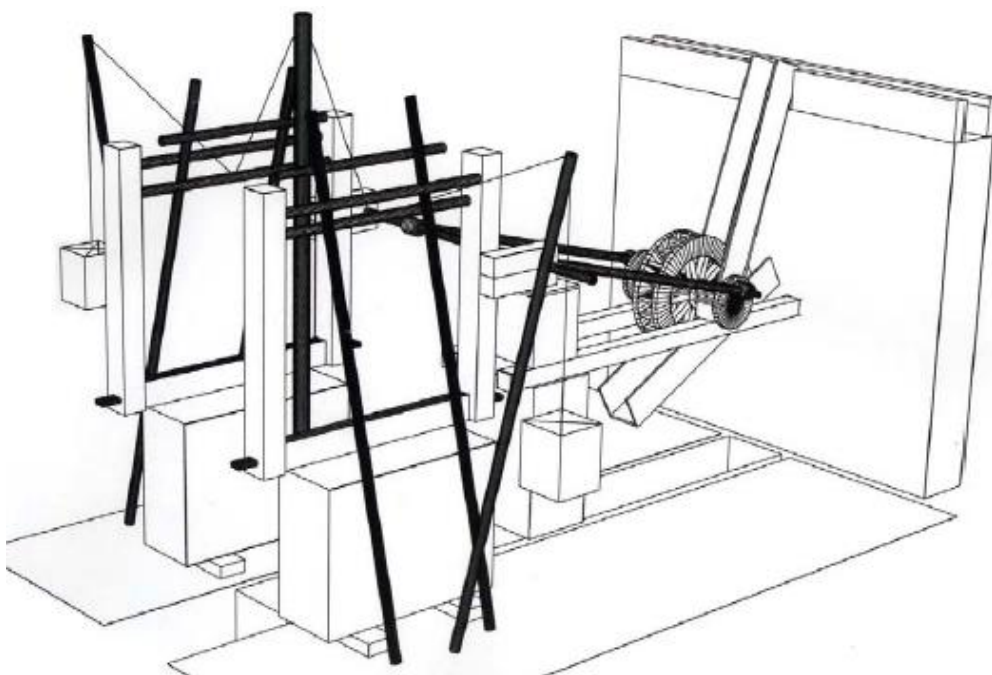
Disseny de la màquina de serrar de Th. Schioler.
